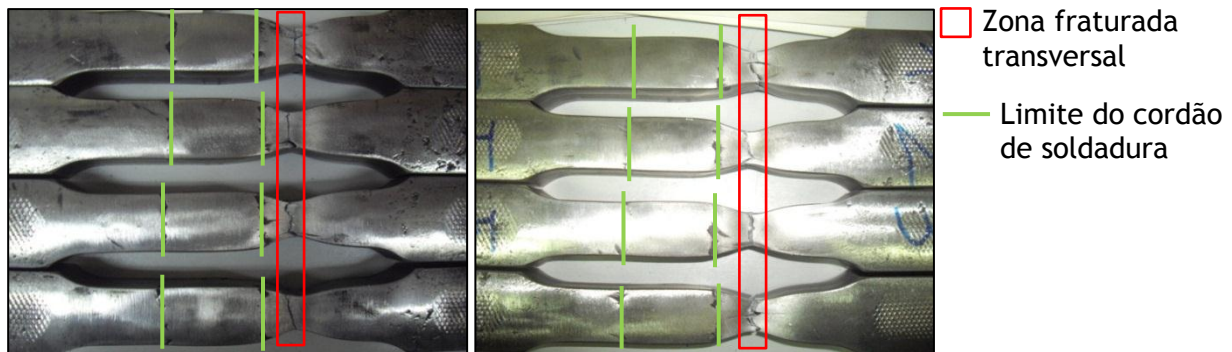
Localização da fratura transversal e do cordão de soldadura na soldadura 1 (esquerda) e 2 (direita)
